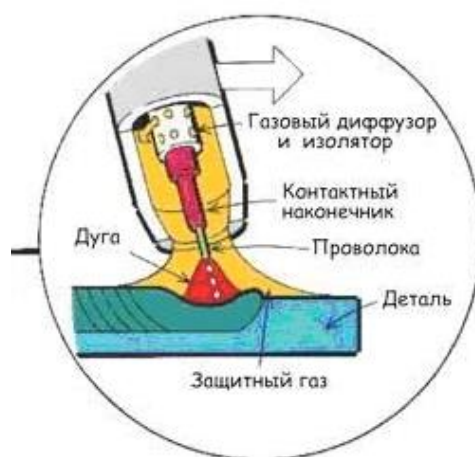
Принципиальная схема сварки в защитных газах плавящимся электродом
